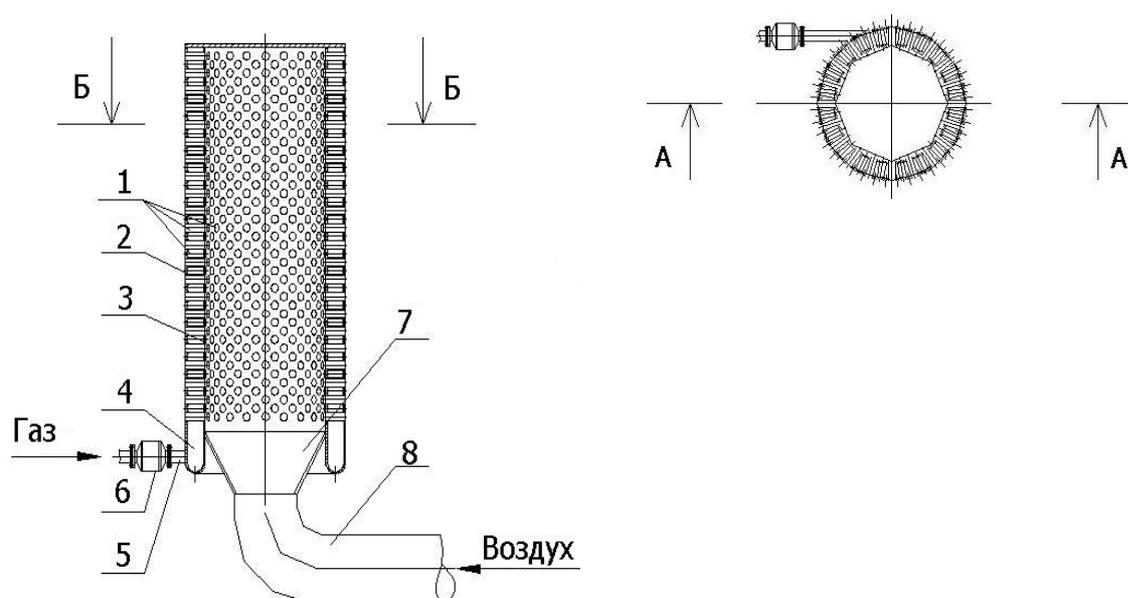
Газогорелочное устройство: 1) воздухопроводы, 2) пористая цилиндрическая поверхность, 3) непористая цилиндрическая поверхность, 4) раздающий газовый коллектор, 5) газопровод, 6) сменный цеолитовый фильтр, 7) диффузор, 8) воздухопровод
